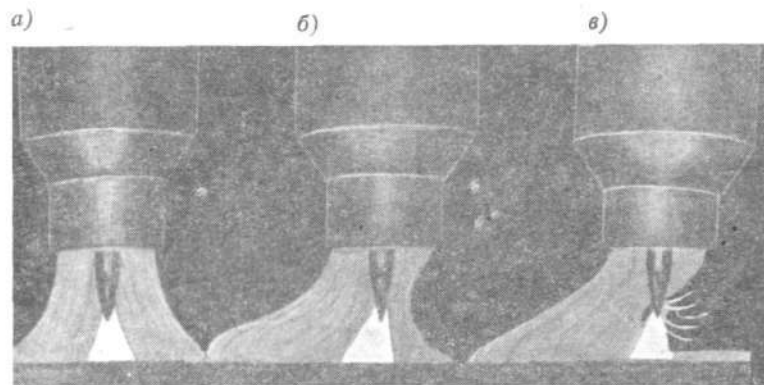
Влияние скорости сварки на эффективность газовой защиты: а) — нормальная; б — повышенная; в) — недопустимо высокая скорость сварки.
